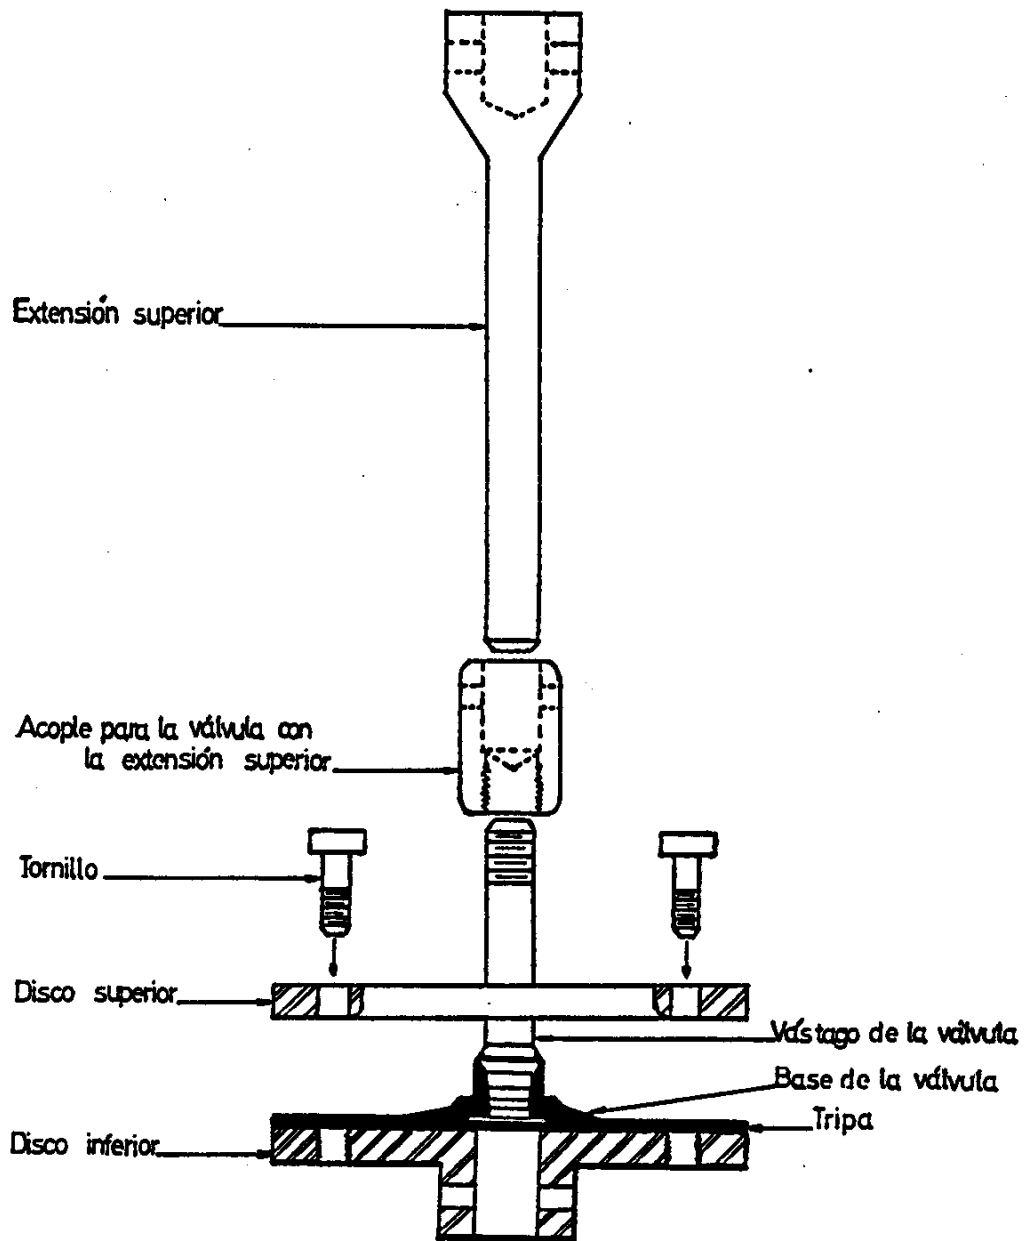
Montaje completo del equipo de ensayo adhesión a la válvula.
